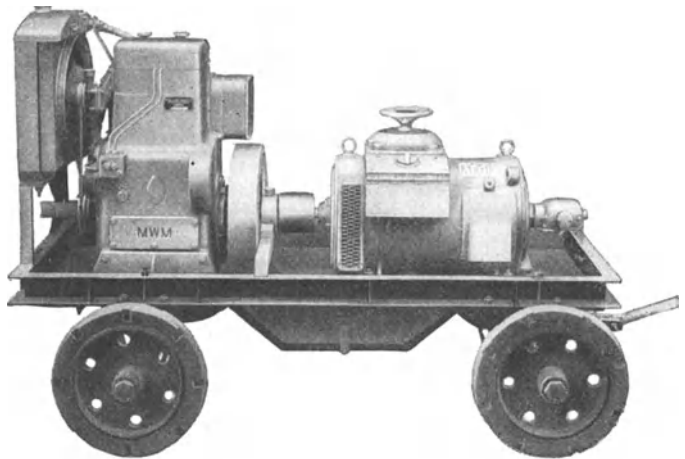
Mit Dieselmotor gekuppelte Schweißmaschine.
